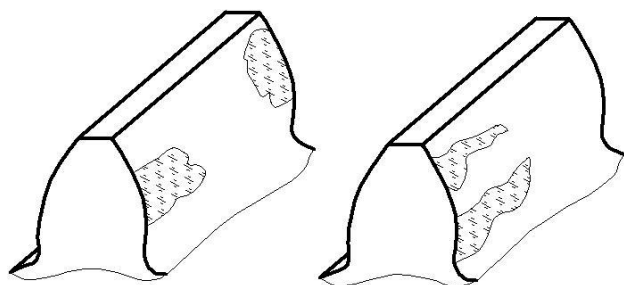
Неприпустимі форми контакту зубів і поломка зубів
